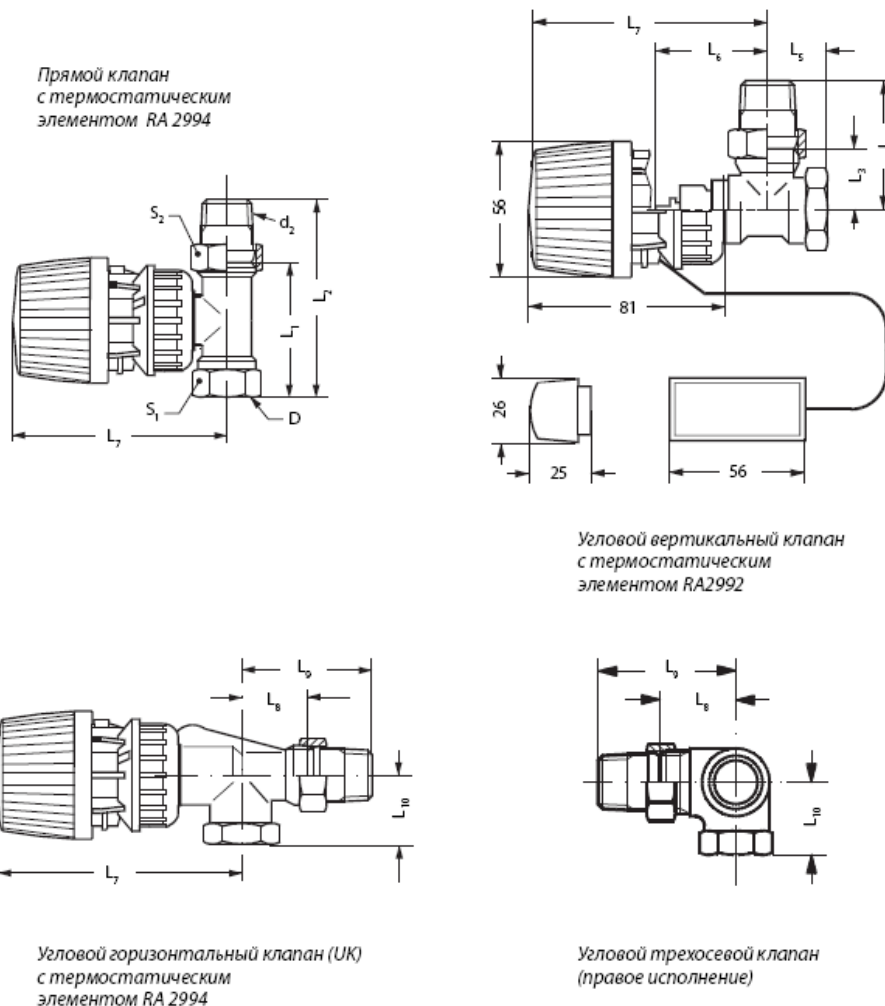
Габаритные и присоединительные размеры клапанов терморегулирующих типа RA-N.
